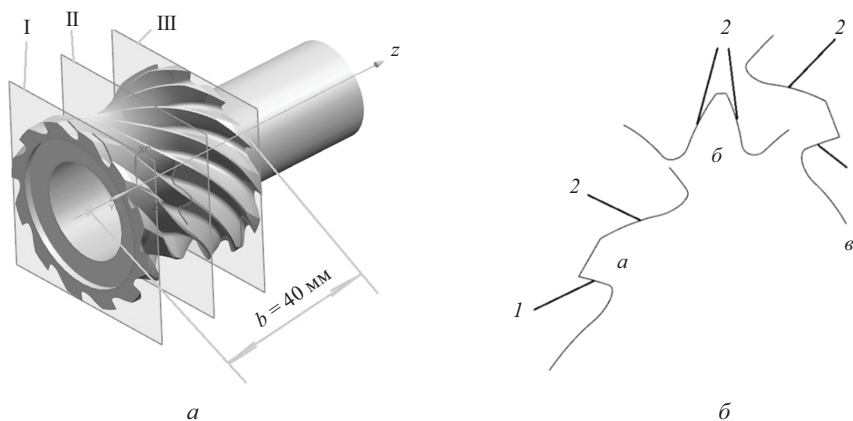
Зубчатое колесо и вспомогательные плоскости, рассекающие боковую поверхность зубьев (а); сечения боковой поверхности зуба (б)
